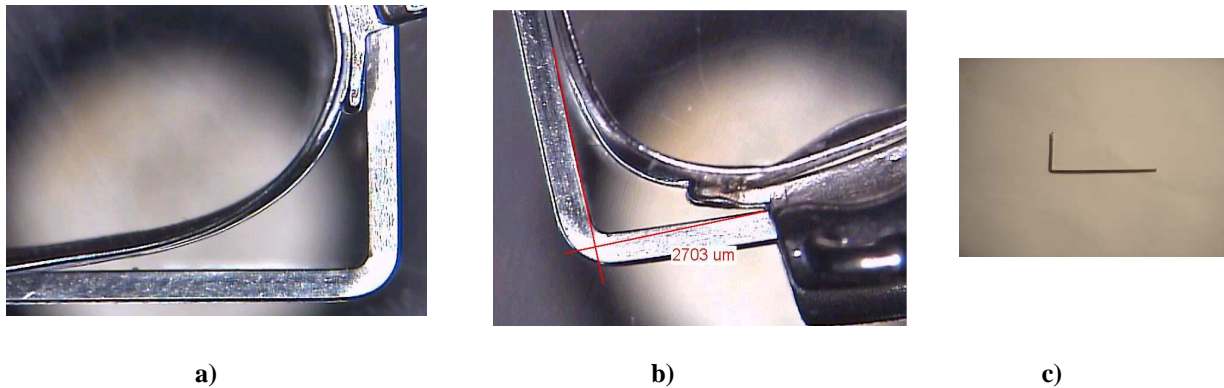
a) Photo und b) Vermessung der Bestimmung der Attachmentlokalisierung mit dem Video-Mess-Inspektionssystem, Firma Jena Engineering; c) passgenauer, um 90° gebogener Winkeldraht
